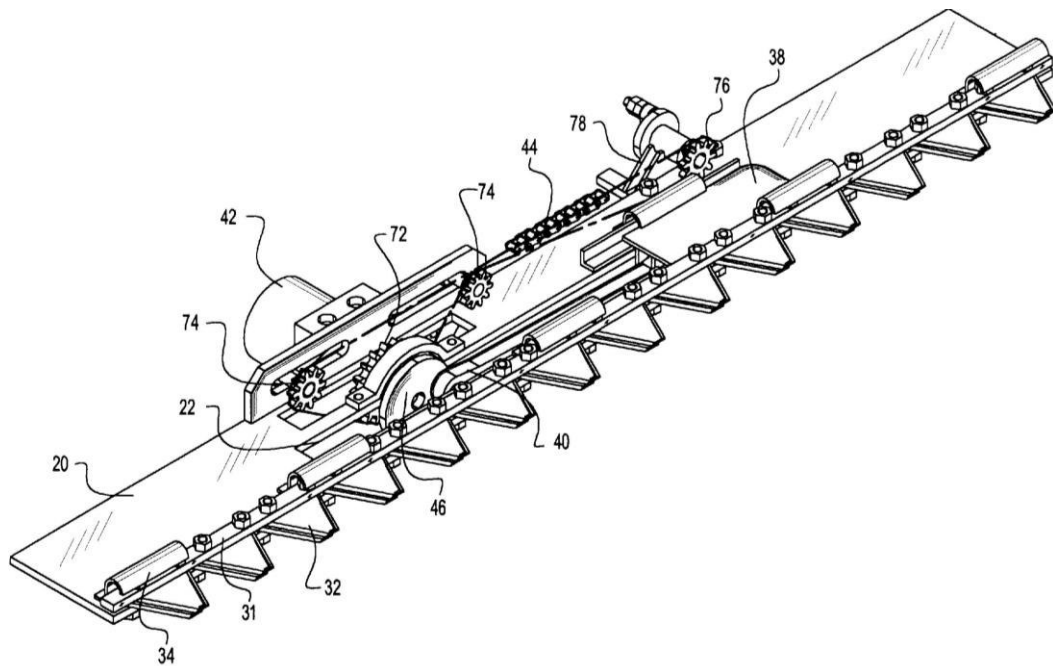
Загальний вигляд несучої плити з верхнім ріжучим елементом
